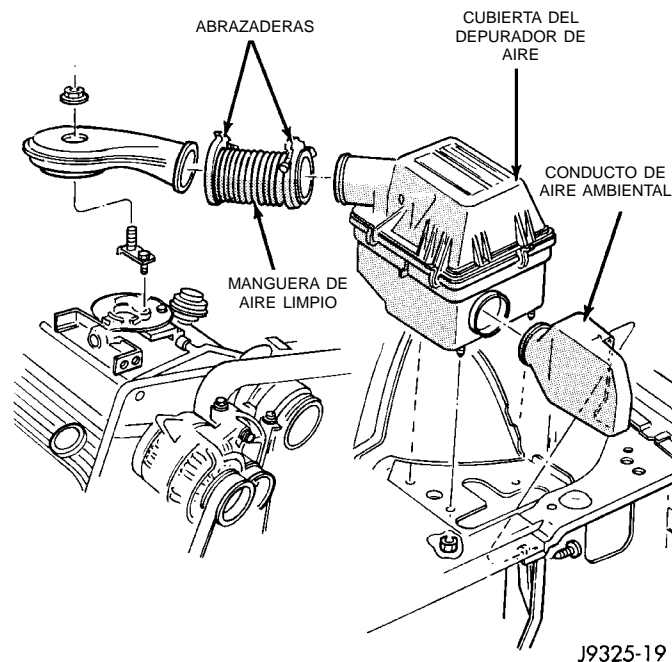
Depurador de aire—Se muestra el motor de 5.2L V-8
